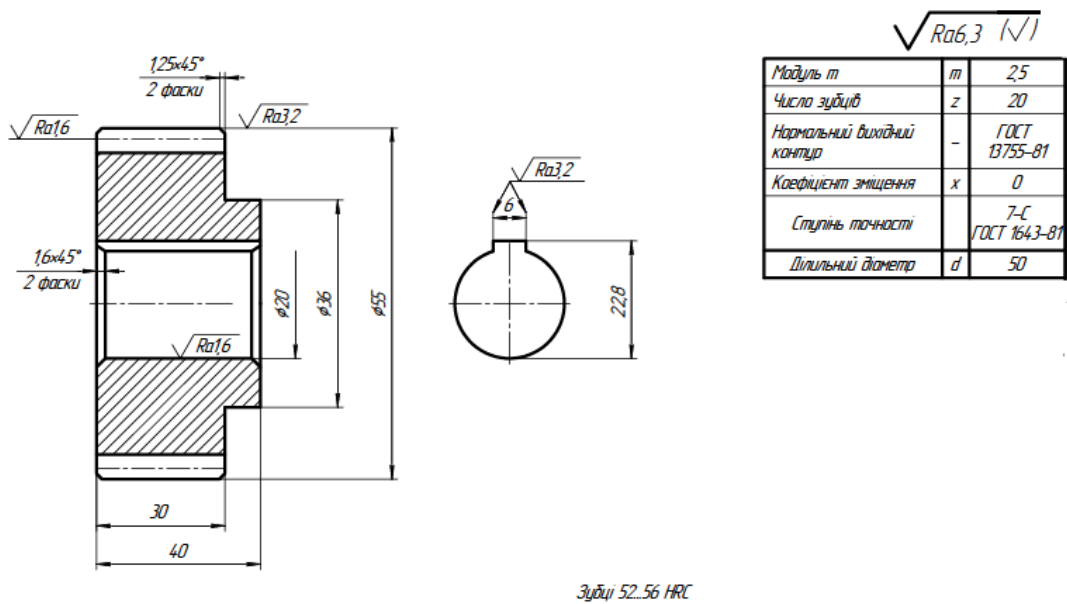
Фрагмент кресленника зубчастого колеса
